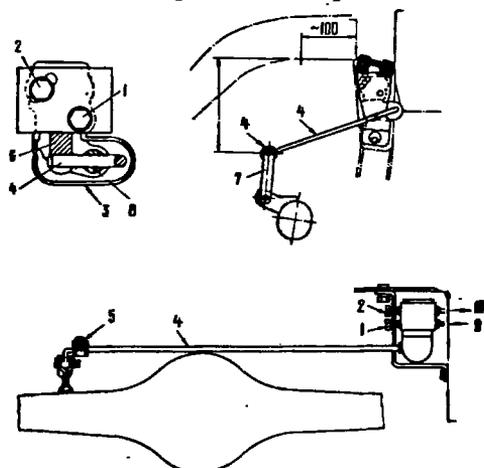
Схема установки регулятора давления задних тормозов и его регулировки: 1, 2 - болты крепления регулятора давления к кронштейну; 3 - защитный колпачок; 4 - торсионный рычаг привода регулятора давления; 5 - кронштейн крепления рычага к кузову; 6 - поршень; 7 - тяга соединения с кронштейном балки заднего моста; 8 - ось; 9 - штуцер трубопровода для подвода тормозной жидкости от главного цилиндра; 10 - штуцер трубопровода для отвода тормозной жидкости в колесные цилиндры; X = 140 ± 5 мм
